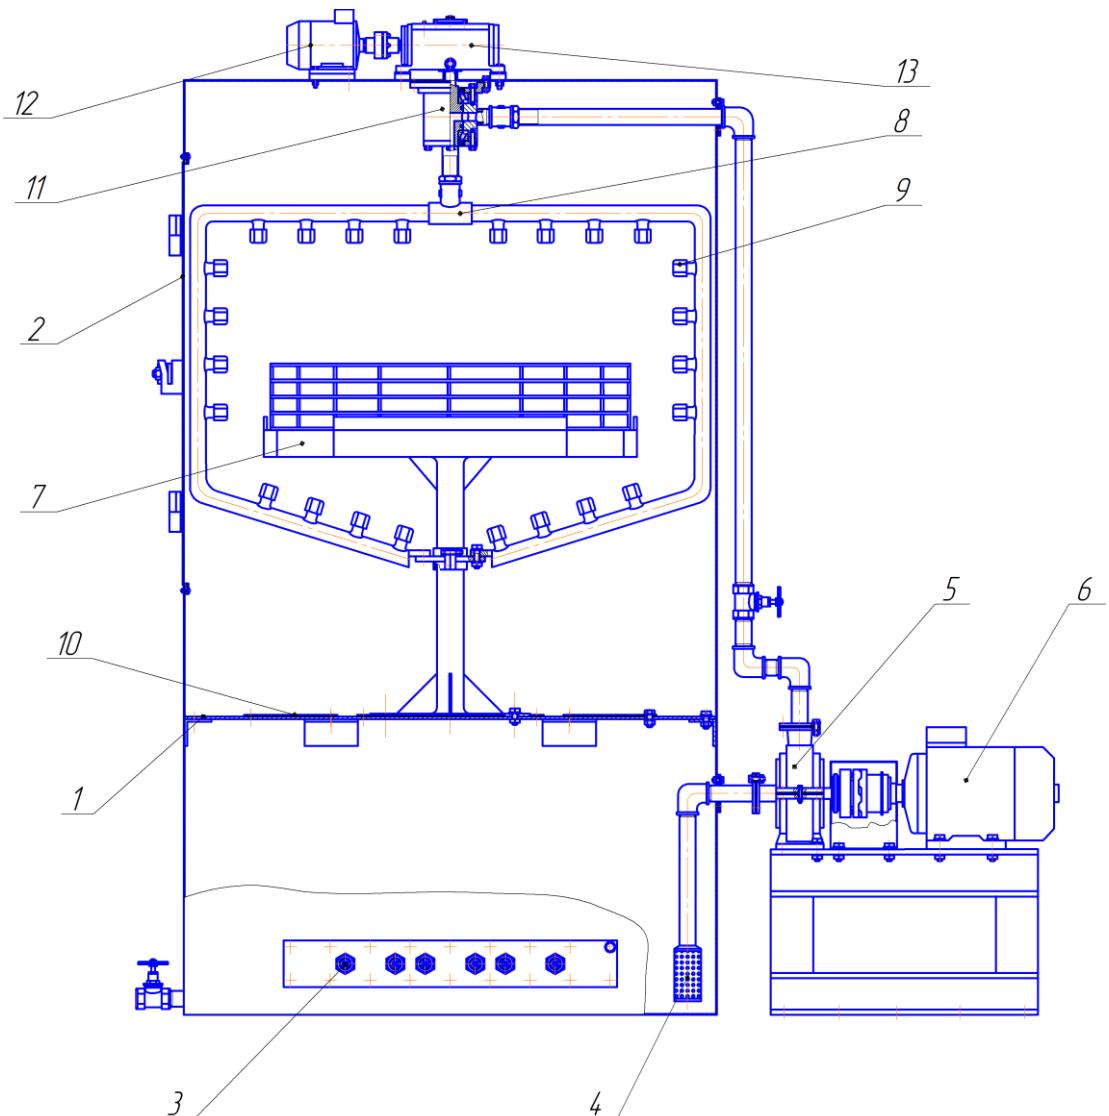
Схема установки для мойки агрегатов: 1-перегородка; 2-корпус; 3-тэн; 4-фильтр; 4-насос; 6,12-электродвигатели; 7-стол; 8-рама; 9-форсунка; 10-фильтрующая сетка; 11-гидромуфта; 13-редуктор;
